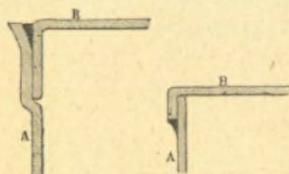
Coupe de boîtes fermées par soudure.
